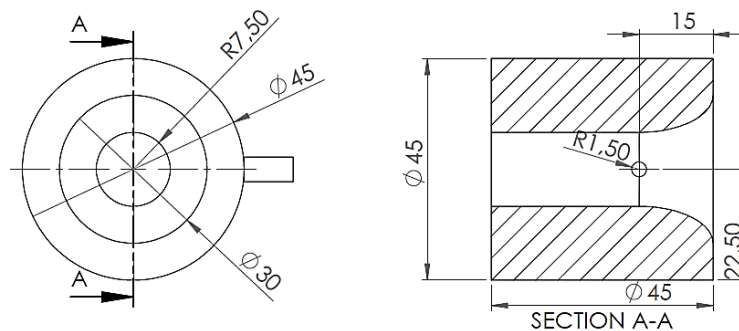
Desenho técnico da tubeira fabricada para o esquentador
